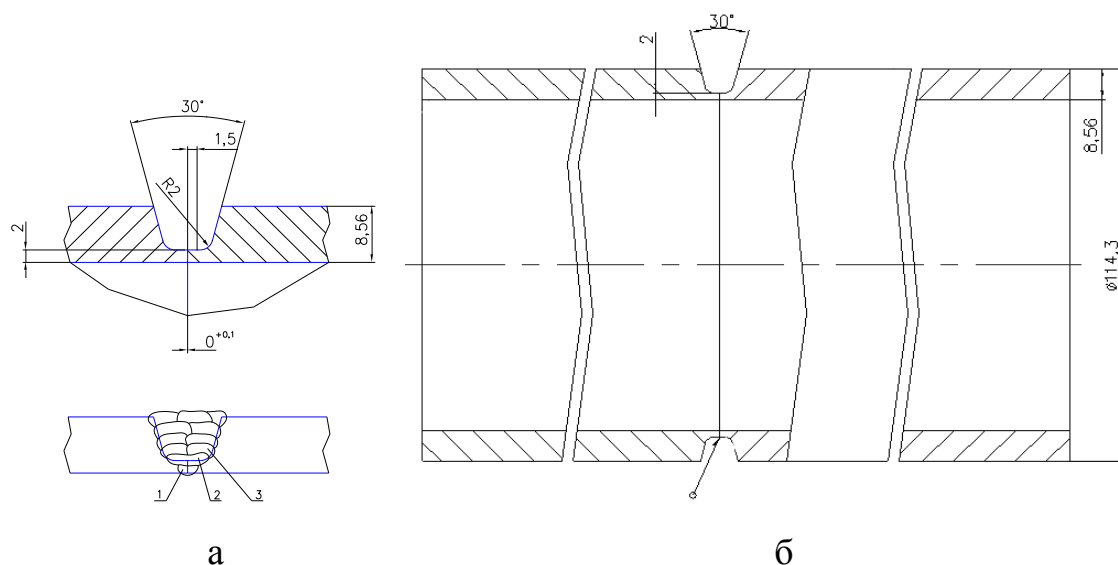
Геометрические параметры сварного соединения – а, эскиз свариваемой трубы с выполненной разделкой кромок – б
